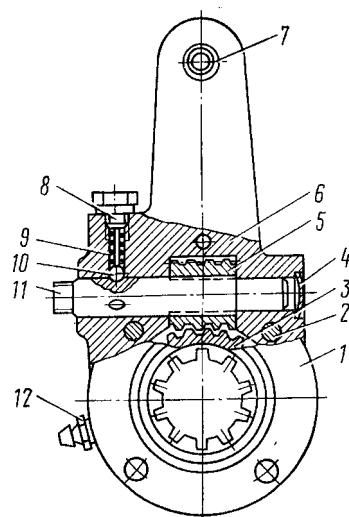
Регулировочный рычаг: 1 - крышка; 2 - заклепка; 3 - колесо зубчатое; 4 - заглушка; 5 - червяк; 6 - корпус; 7 - втулка; 8 - болт стопорный; 9 - пружина фиксатора; 10 - шарик фиксатора; 11 - ось червяка; 12 - масленка
